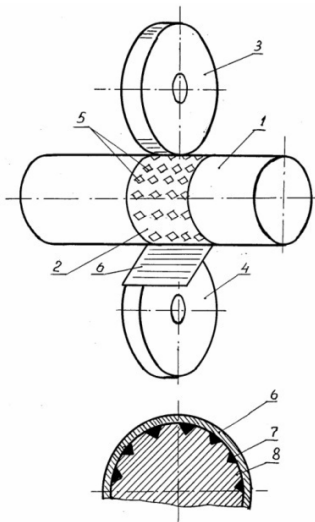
Существующая схема восстановления изношенных поверхностей: 1 – деталь; 2 – изношенная поверхность; 3 и 4 – сварочные ролики; 5 – ячейки насечки; 6 – лента; 7 – впадины с припоем; 8 – гребни
